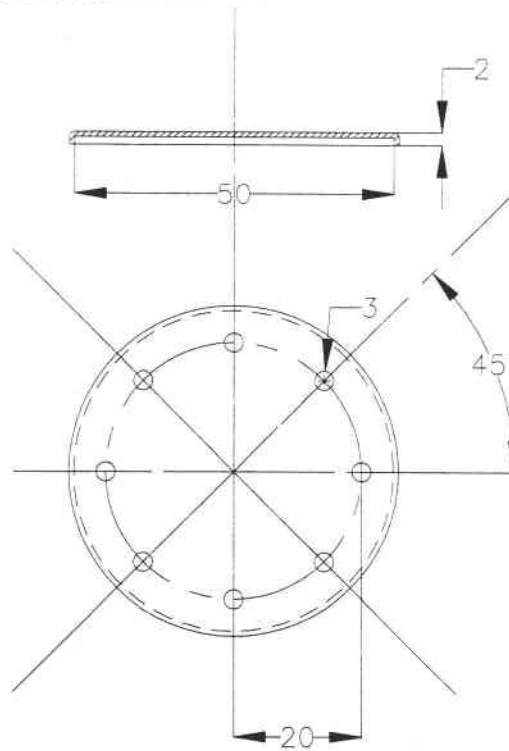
Définition de la géométrie des éprouvettes utilisées en emboutissage
